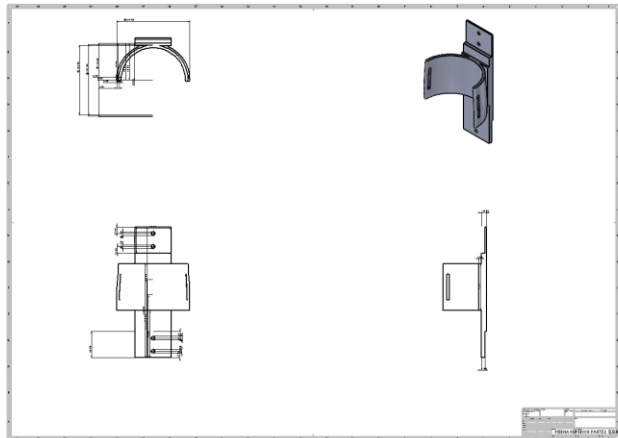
Perspectiva isométrica y vistas diédricas de la pieza 3.
